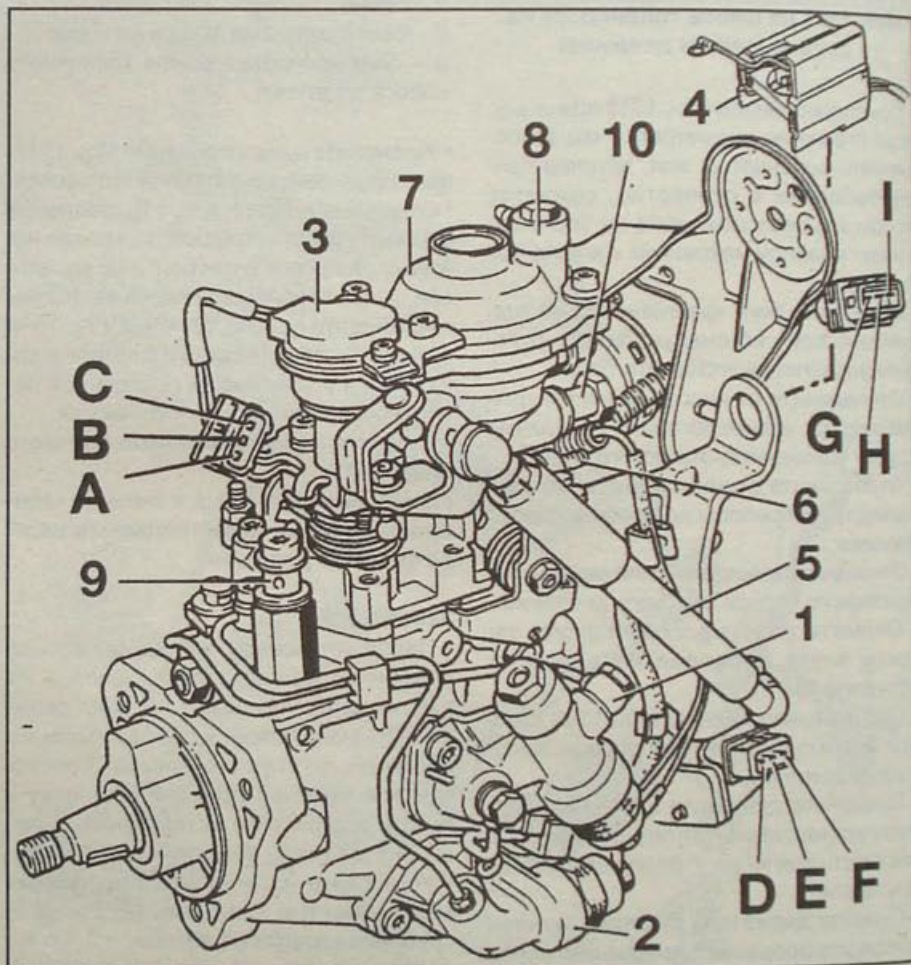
Топливный насос высокого давления (двигатель G8T 716):
